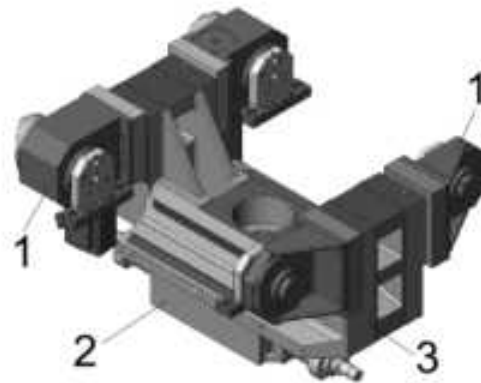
Schema Werkstückwechsler mit IWW-Grundvorrichtung
